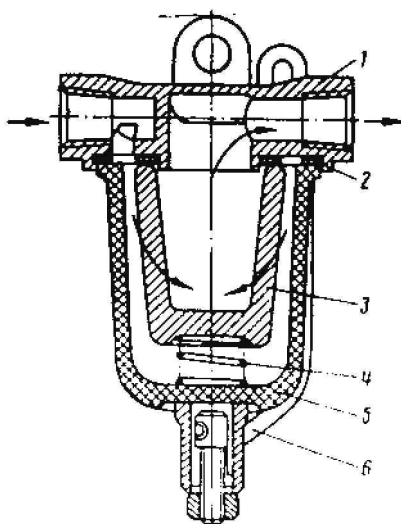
Фильтр тонкой очистки топлива: 1-корпус фильтра; 2-прокладка; 3-фильтрующий элемент; 4-пружина; 5-стакан-отстойник; 6-зажим стакана.
